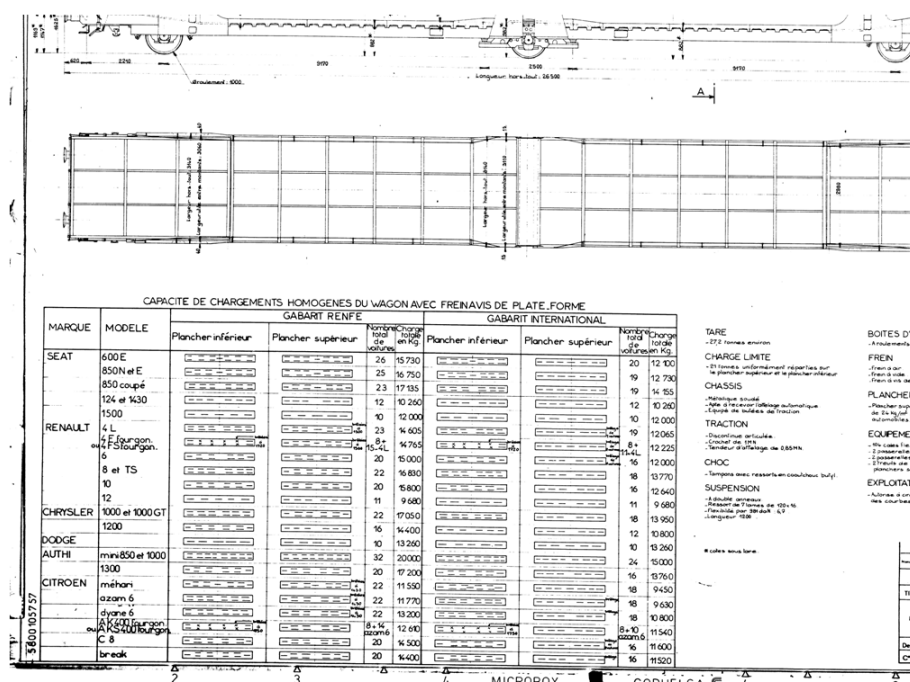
Detalle de plano donde se aprecia la distribución de los automóviles
